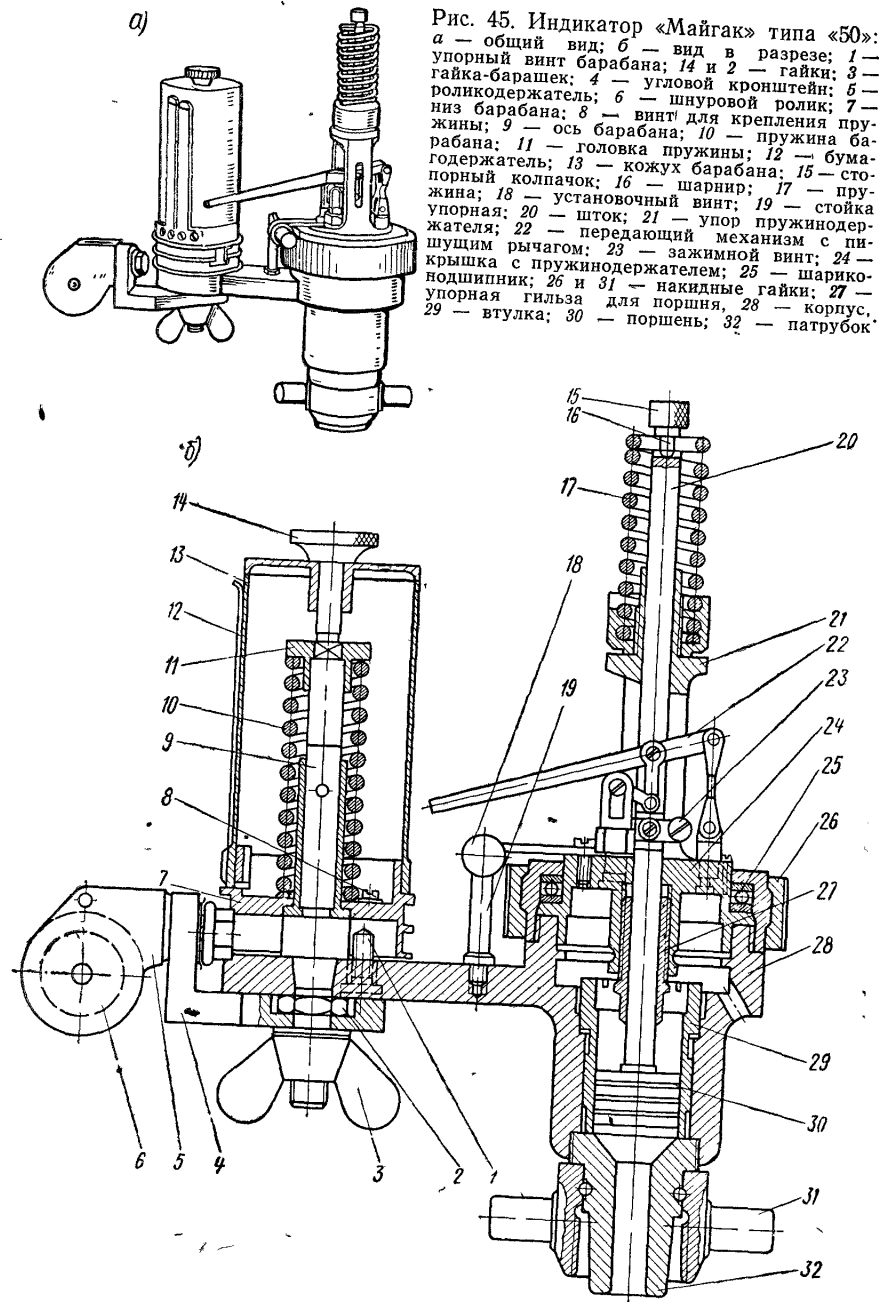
Индикатор «Майгак» типа «50»: а — общий вид; б — вид в разрезе; 1 — упорный винт барабана; 14 и 2 — гайки; 3 — гайка-барашек; 4 — угловой кронштейн; 5 — роликодержатель; 6 — шнуровой ролик; 7 — низ барабана; 8 — винт для крепления пружины; 9 — ось барабана; 10 — пружина барабана; 11 — головка пружины; 12 — бумагодержатель; 13 — кожух барабана; 15 — стопорный колпачок; 16 — шарнир; 17 — пружина; 18 — установочный винт; 19 — стойка упорная; 20 — шток; 21 — упор пружинодержателя; 22 — передающий механизм с пишущим рычагом; 23 — зажимной винт; 24 — крышка с пружинодержателем; 25 — шарико-подшипник; 26 и 31 — накидные гайки; 27 — упорная гильза для поршня; 28 — корпус; 29 — втулка; 30 — поршень; 32 — патрубок.
